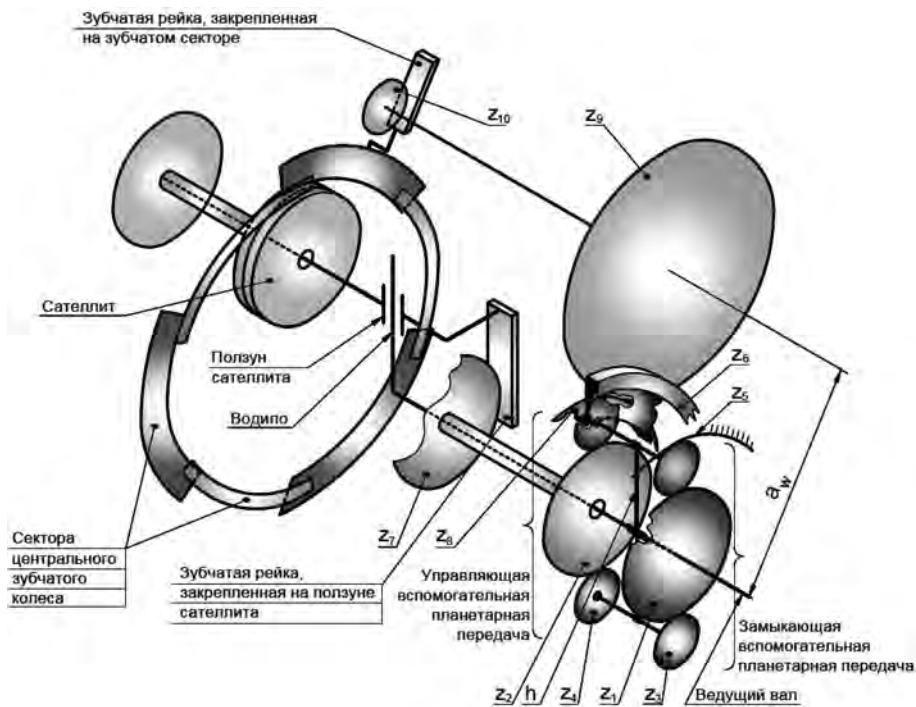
Схема механической передачи механизма регулирования передаточного отношения
